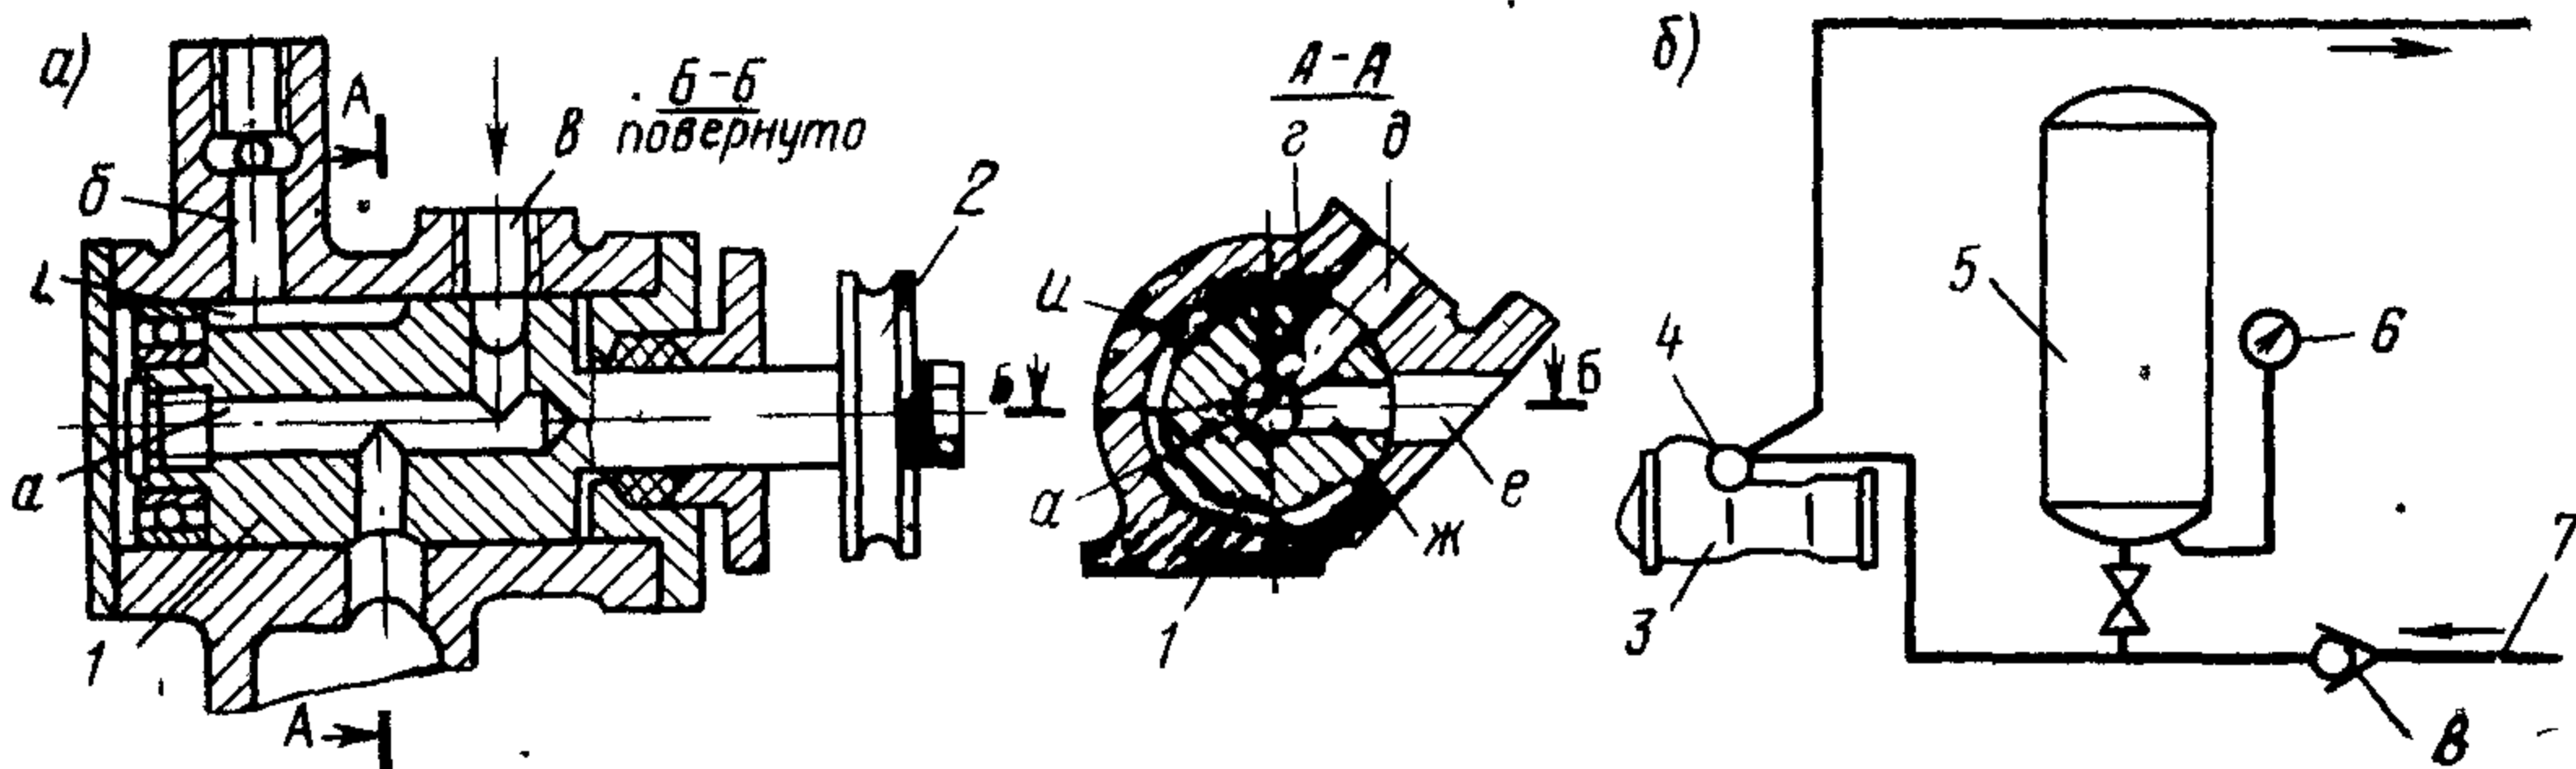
Золотник и схема питания ДУ двигателя ЗД6
